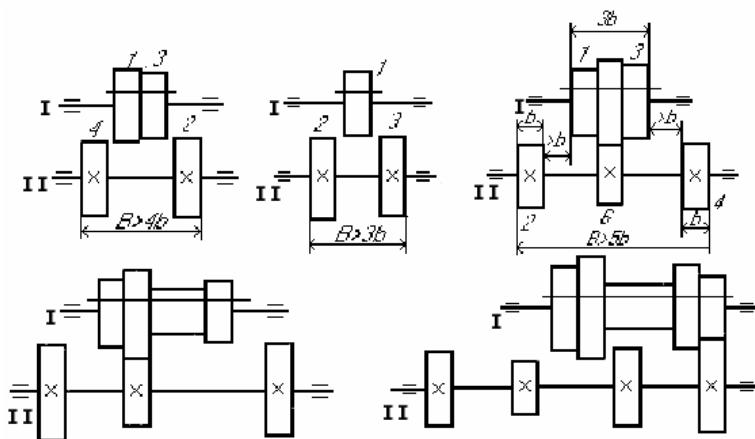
Коробки передач с передвижными многовенцовыми блоками зубчатых колес
